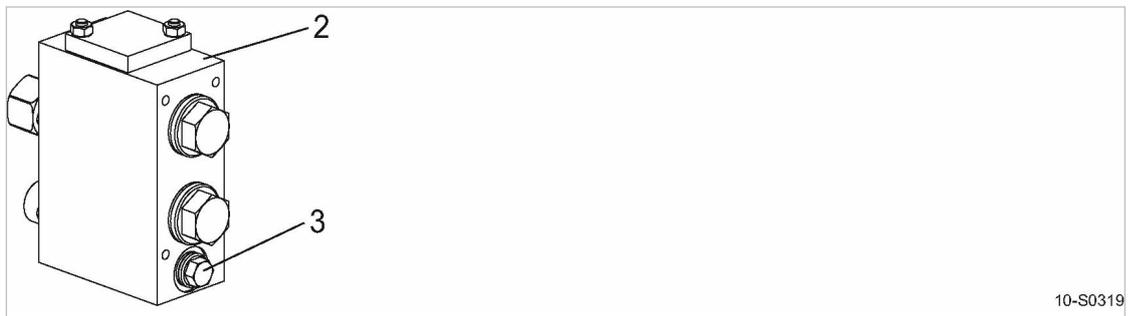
Kühllöl wechseln, Wärme-Rückgewinnung
